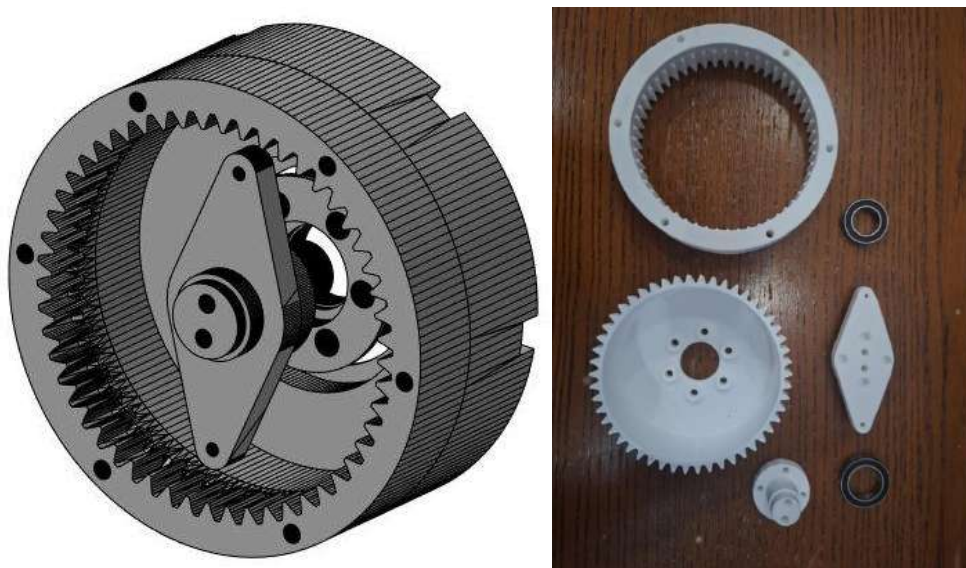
3D-модель и напечатанный вариант гармонического редуктора
